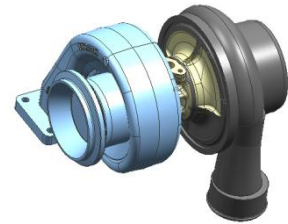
Schéma d'encombrement du turbocompresseur
